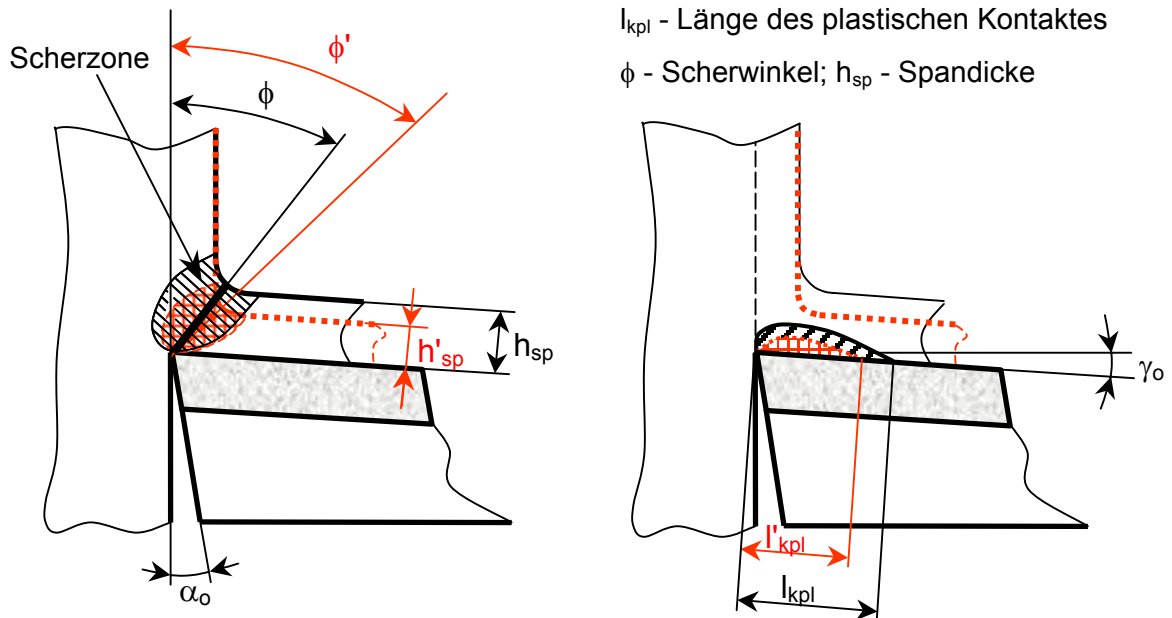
Änderung der Scherzone bzw. der Kontaktlänge des Spanes mit der Spanfläche des Werkzeuges infolge des Spanens mit beschichtetem Werkzeug (gestrichelte Linien und Bezeichnungen mit Strichen beziehen sich auf das beschichtete Werkzeug)
